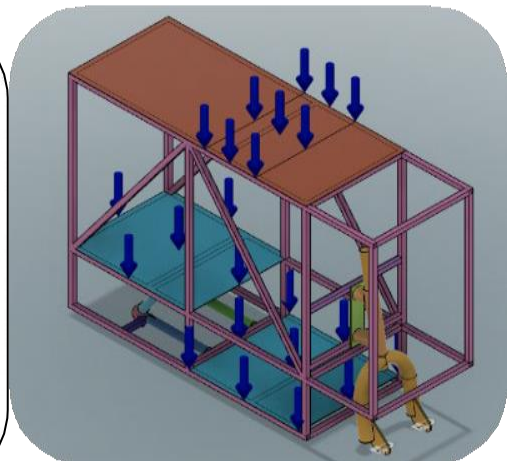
Ubicación de las cargas aplicadas a la estructura
